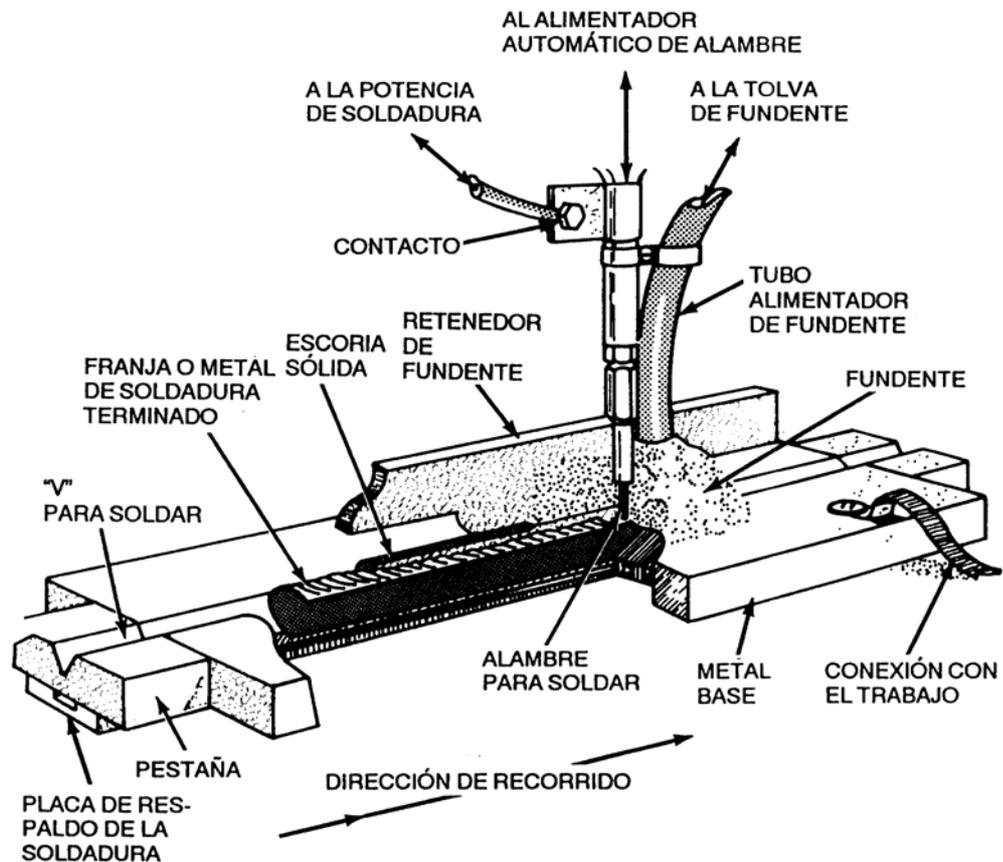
Esquema del proceso de soldadura por arco sumergido
